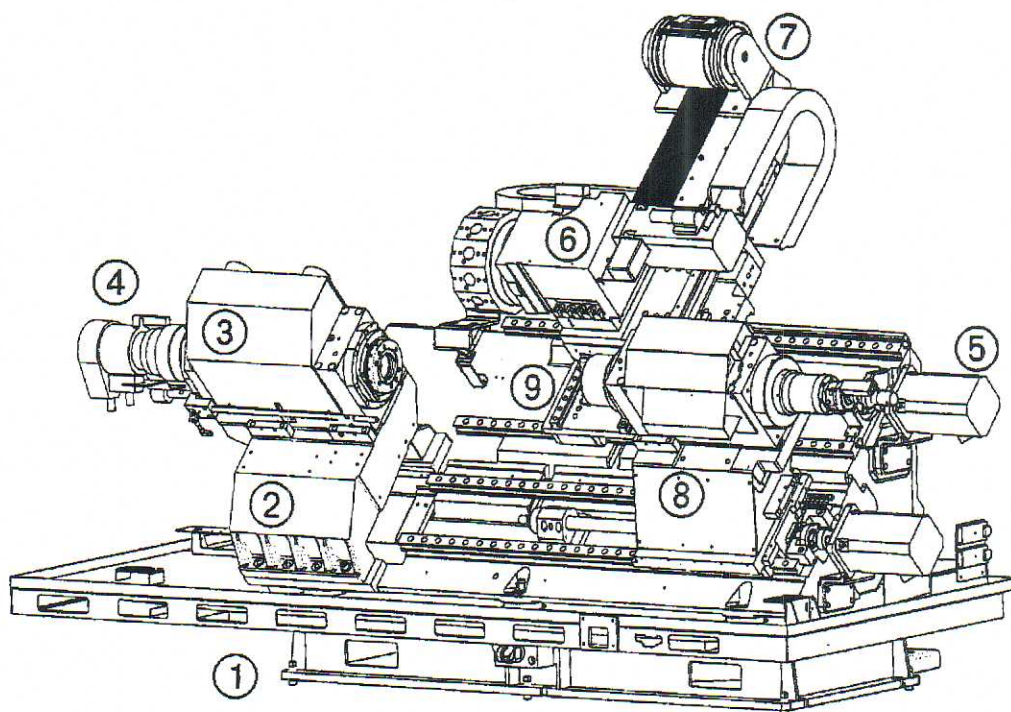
Проставить номера базовых деталей и механизмов станка с ЧПУ
